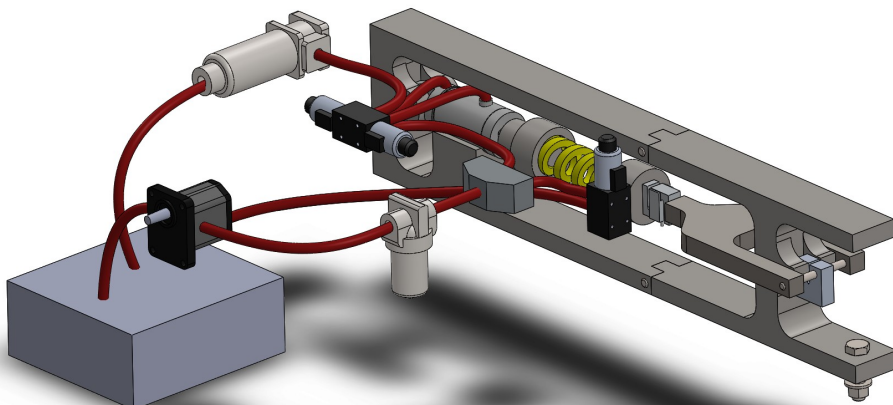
imagen del montaje completo de la máquina hidráulica.
